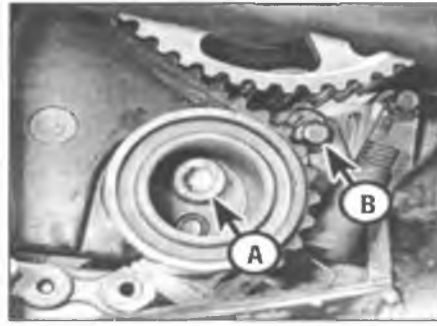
Болты натяжного шкива (А) и щитка (В)
